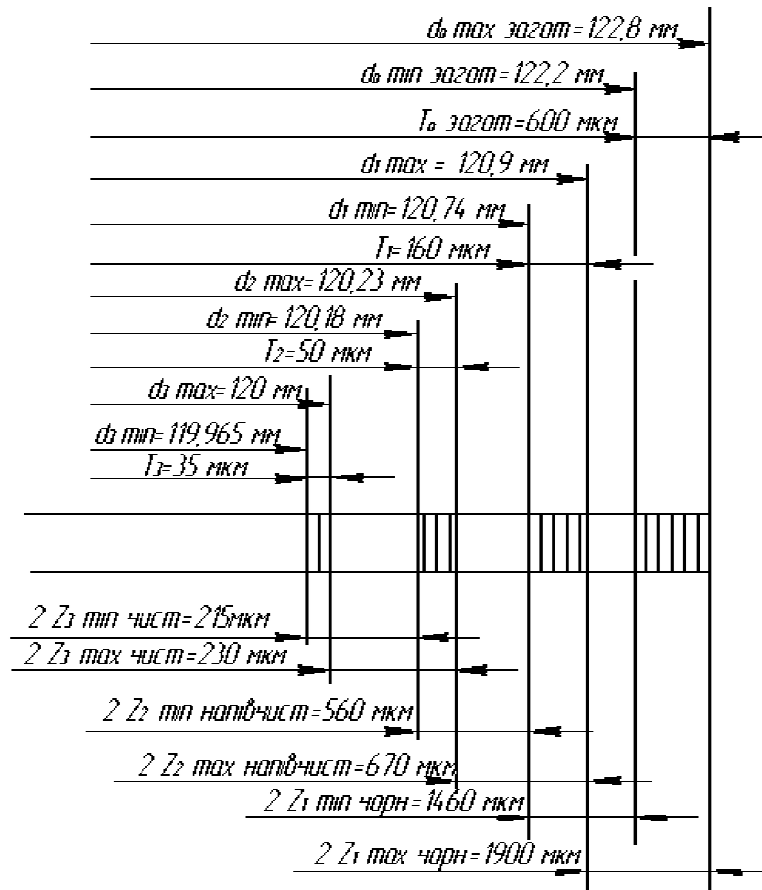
Схема розташування припусків і допусків на оброблення поверхні  $\varnothing 120h7$
